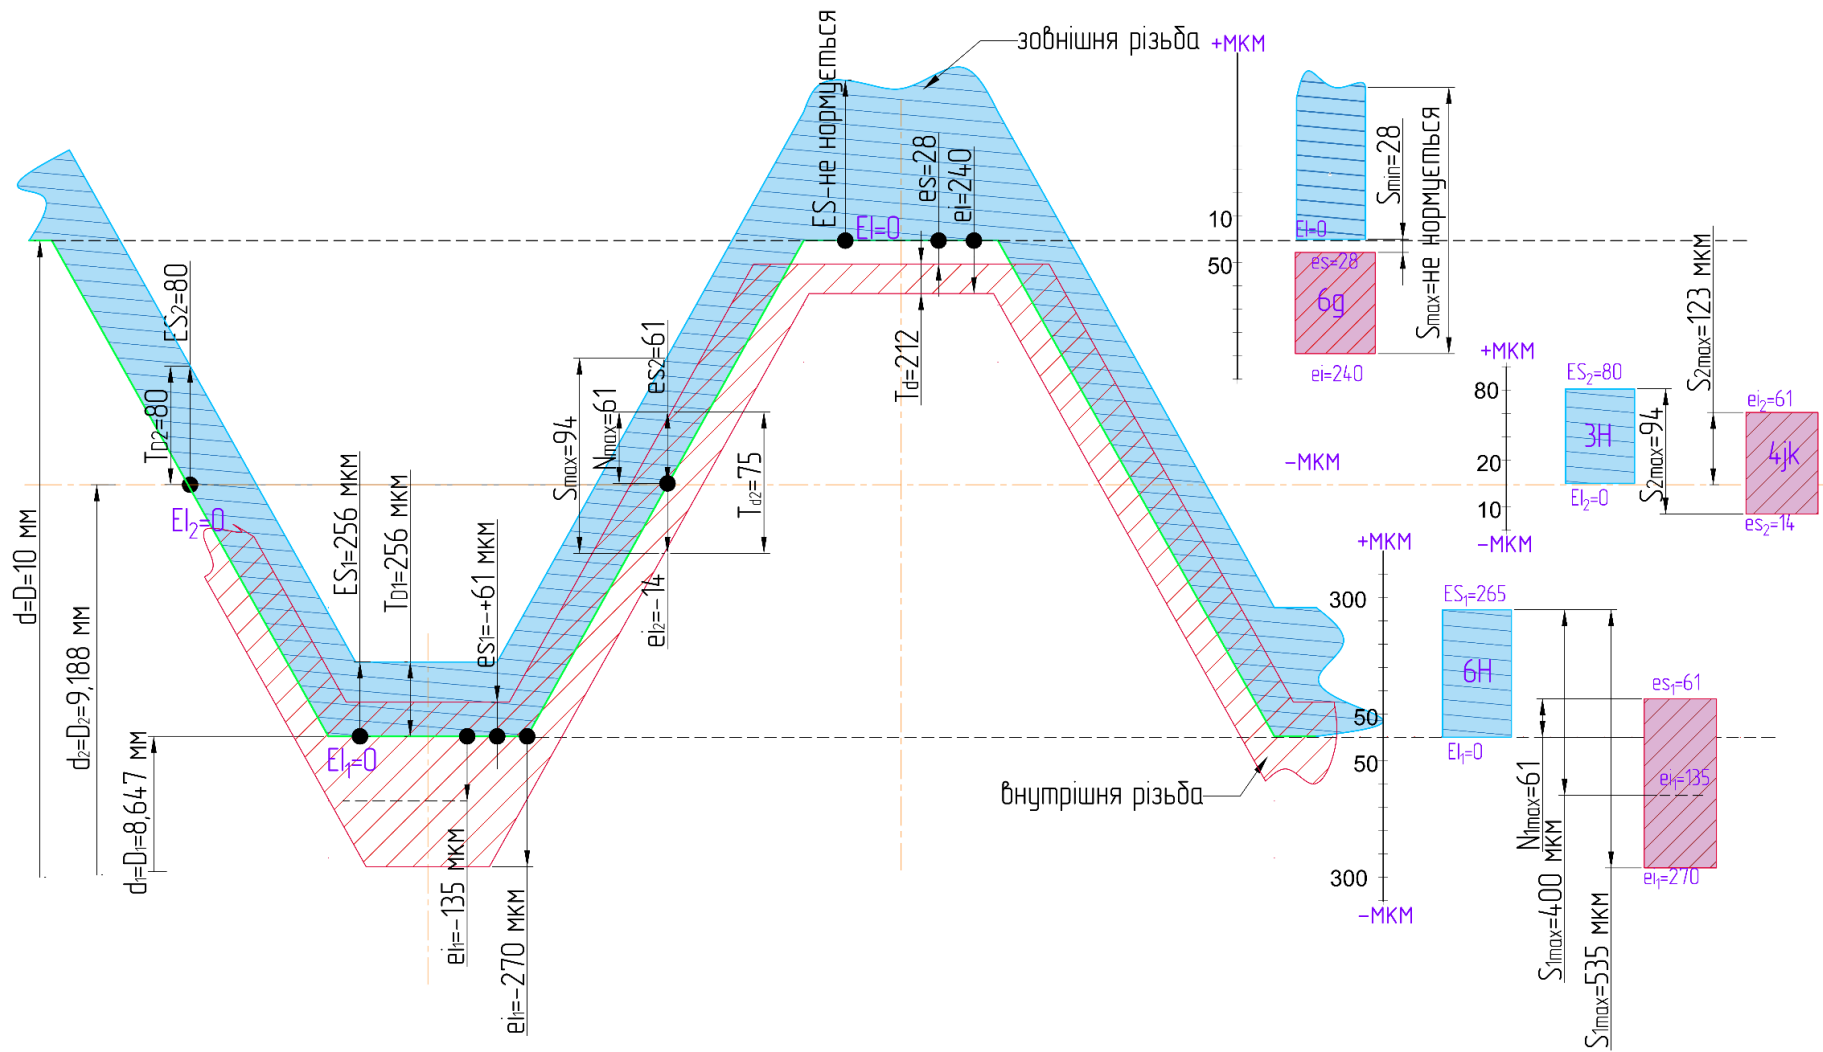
Схема розташування полів допусків за основними діаметрами внутрішньої нарізі $M10 \times 1,25 - \frac{3H6H}{4jk}$
